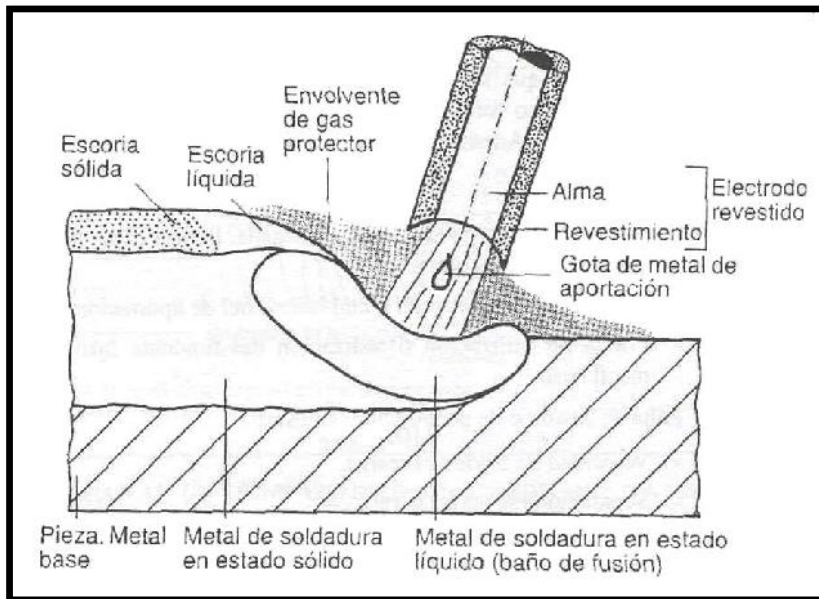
Soldadura SMAW utilizada en gasoductos
